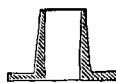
Coupe horizontale de la plaque avec ajutage de la figure 82.
